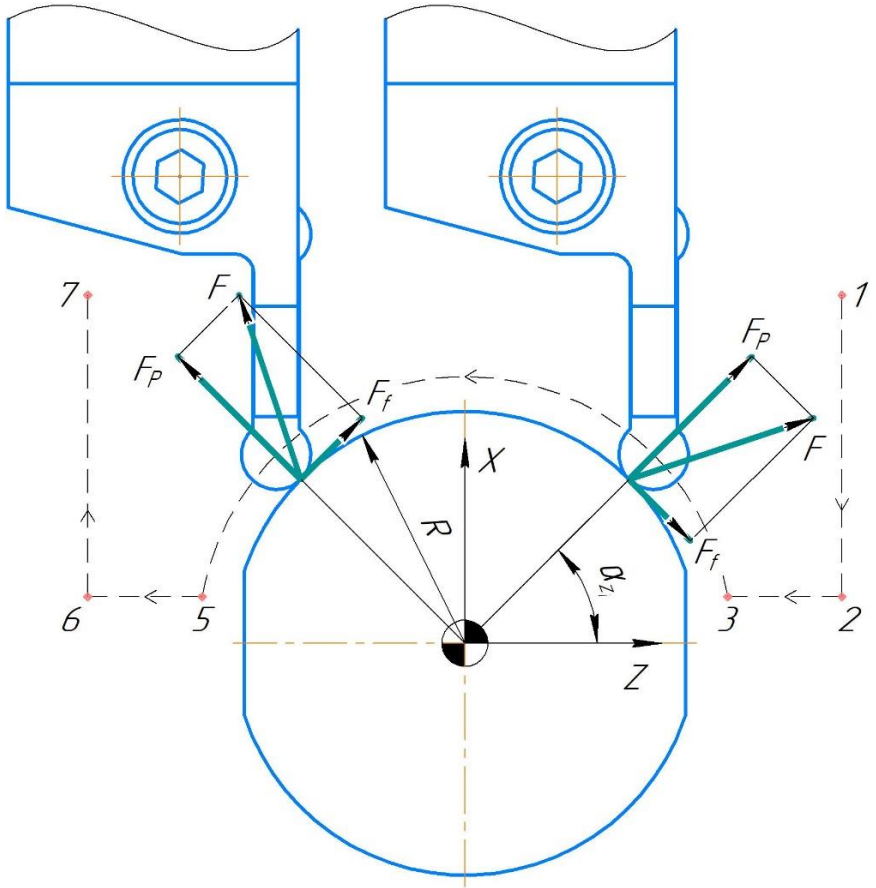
Схема обробки сферичного елемента деталі «Поплавок»
